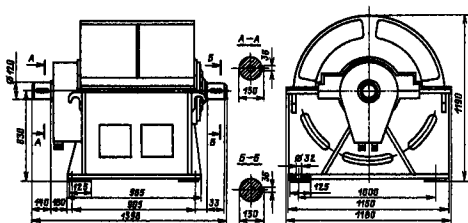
27 Габаритные и установочно-присоединительные размеры муфты ЭМС-750
